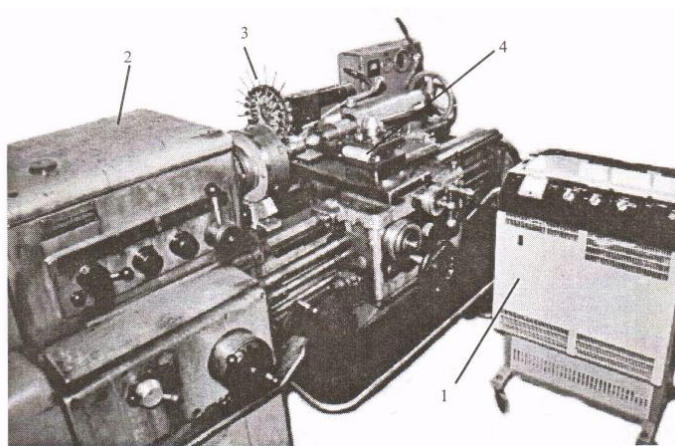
Внешний вид установки ЭЛИТРОН—354
